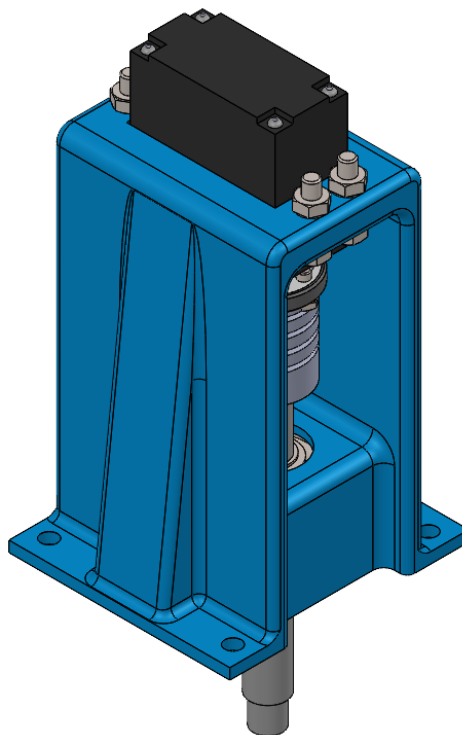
Sous-ensemble porte-servomoteur de la plateforme mobile
